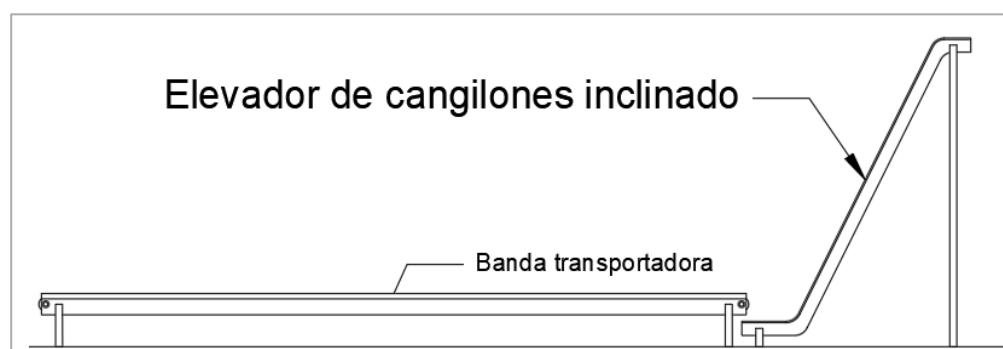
Elevador de cangilones inclinado. [Elaboración propia]
